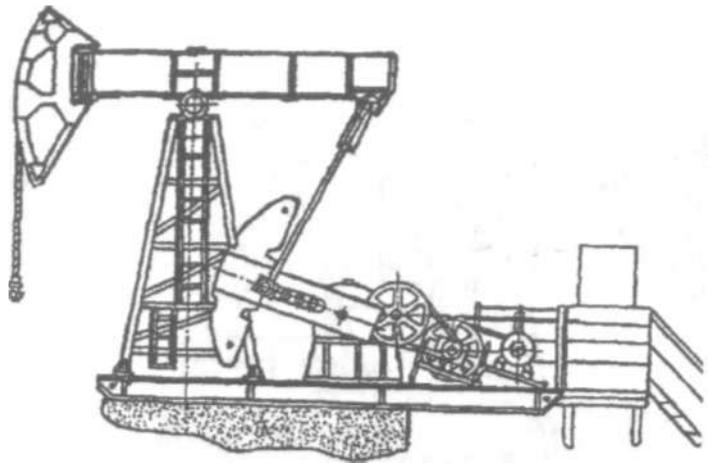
Схема тихоходного станка - качалки с дополнительной ременной передачей
